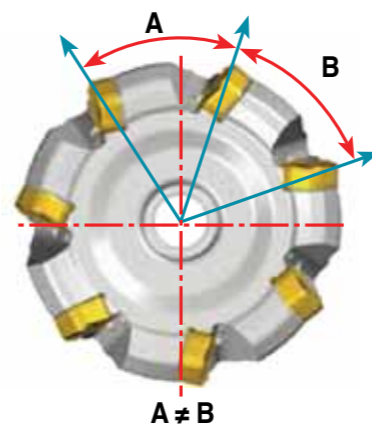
Неравномерный шаг пластин на фрезе Chase12Mill
